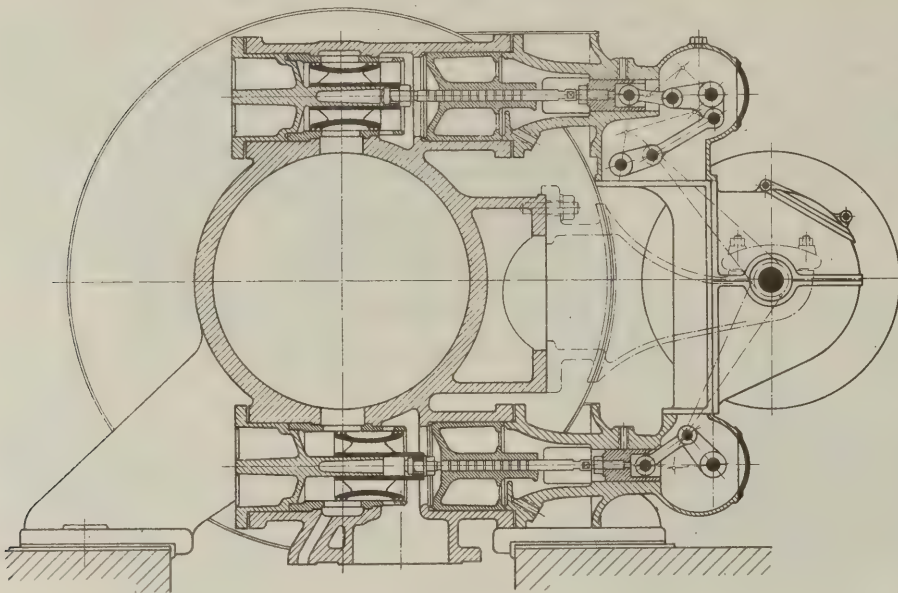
Zwangsläufige Kolbenventilsteuerung mit Achsenregler Patent Proell, gekapselte Bauart mit herausnehmbaren Zylinderdeckeln.
